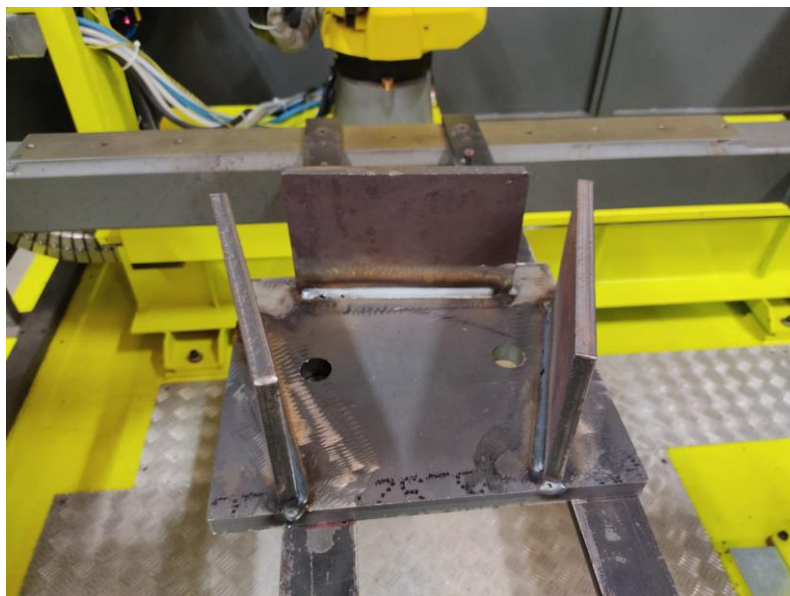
Provede de soldadura usado na visita à Motofil
